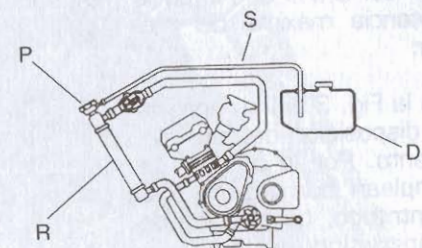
Disposición de un depósito auxiliar de líquido refrigerante, denominado normalmente "bote de expansión".
